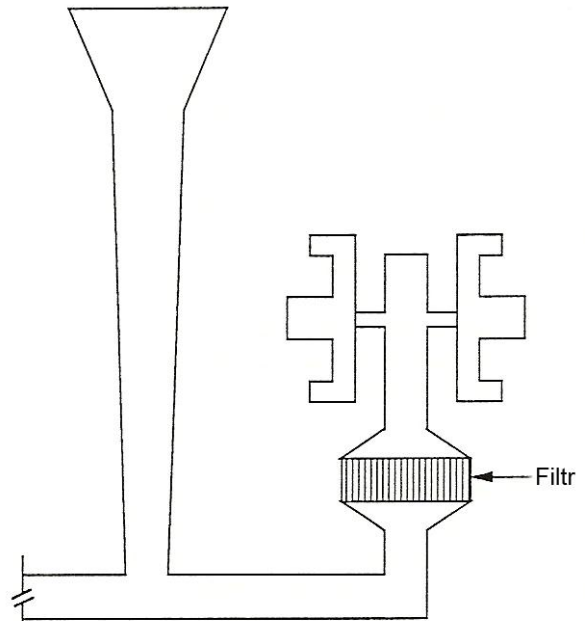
Způsoby odlévání skořepinových forem [5]
